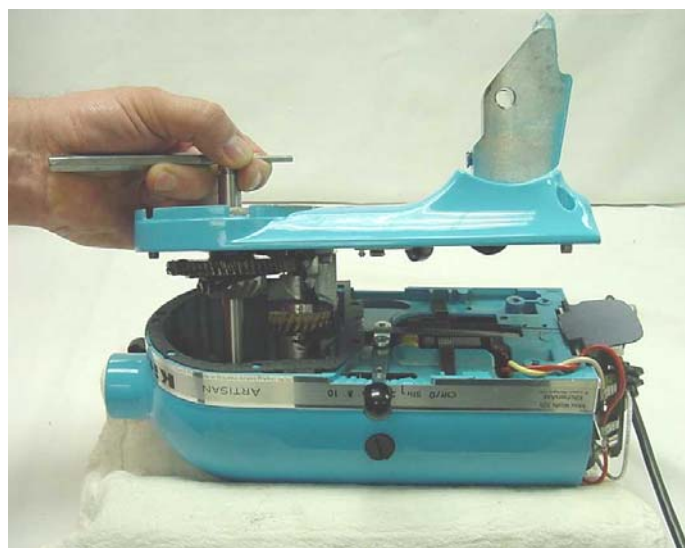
Untere Getriebeabdeckung und Getriebe-/Motorgehäuse zunächst vorsichtig zusammenführen. Welle in das obere Lager einführen. Einen Durchschlag in die Zentralwelle stecken und beim Zusammendrücken leicht hin- und herdrehen, damit sich die Zahnräder ausrichten.
